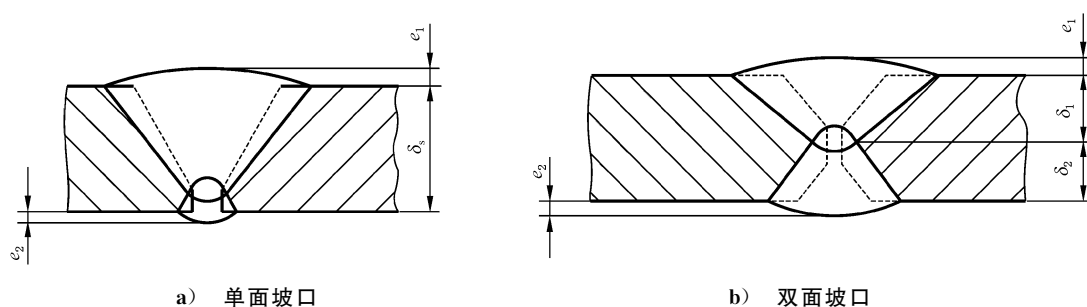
A 类、B 类焊接接头的焊缝余高
